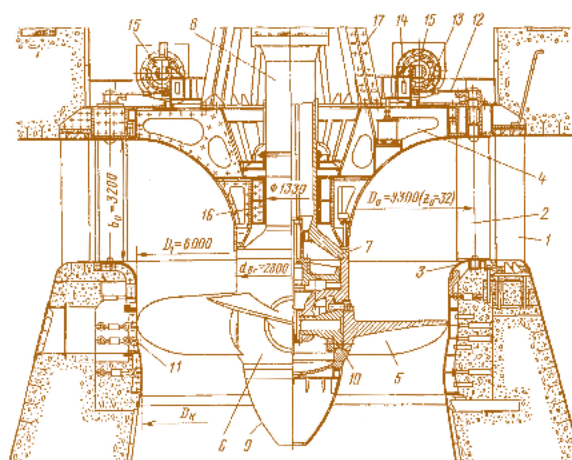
Розріз по поворотно-лопатевій турбіні Кременчуцької ГЕС: 1 – колони статора; 2 – напрямні лопатки; 3 – нижнє кільце; 4 – кришка турбіни; 5 – лопаті робочого колеса; 6 – корпус робочого колеса; 7 – фланець вала; 8 – вал; 9 – обтічник робочого колеса; 10 – камера робочого колеса; 11 – висувний сегмент; 12 – важіль напрямної лопатки; 13 – серга; 14 – регулююче кільце; 15 – сервомотори; 16 – підшипник; 17 – опорна конструкція під'ятника генератора
